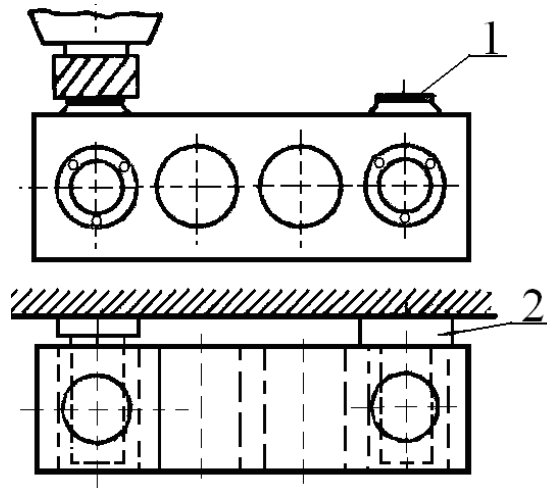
Схема встановлення корпусної деталі на два необроблені отвори з паралельними осями.
